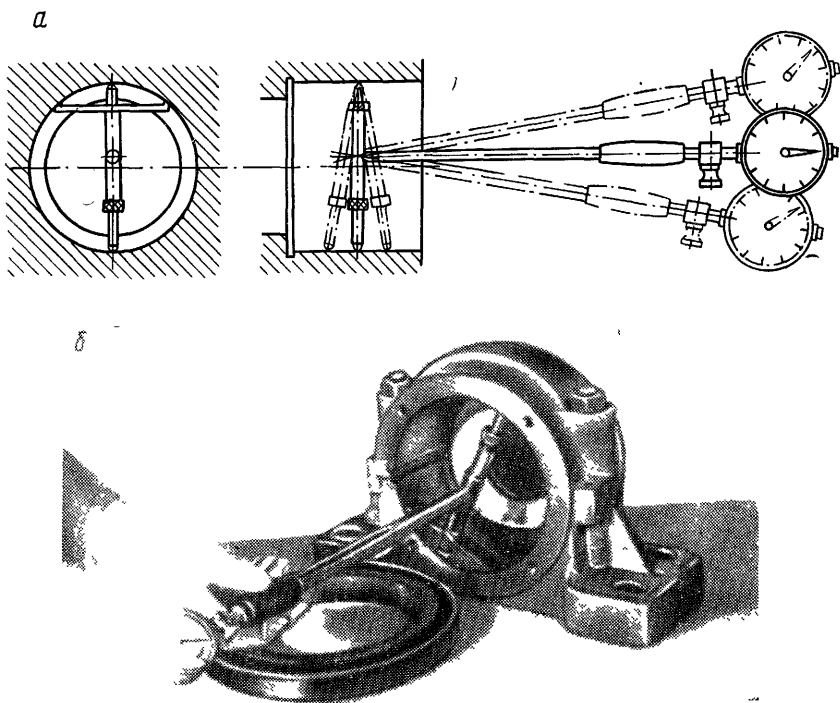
Контроль посадочных мест корпуса подшипника индикаторным нутромером:
